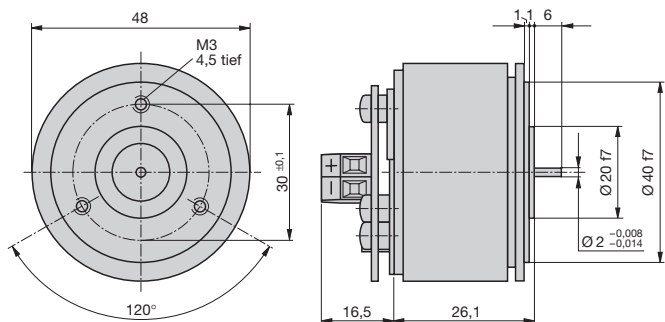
KINAX 2W2 mit Standard-Antriebswelle nur vorn, Ø 2 mm, Länge 6 mm. Anschlussvariante mit Schraubklemmen.
